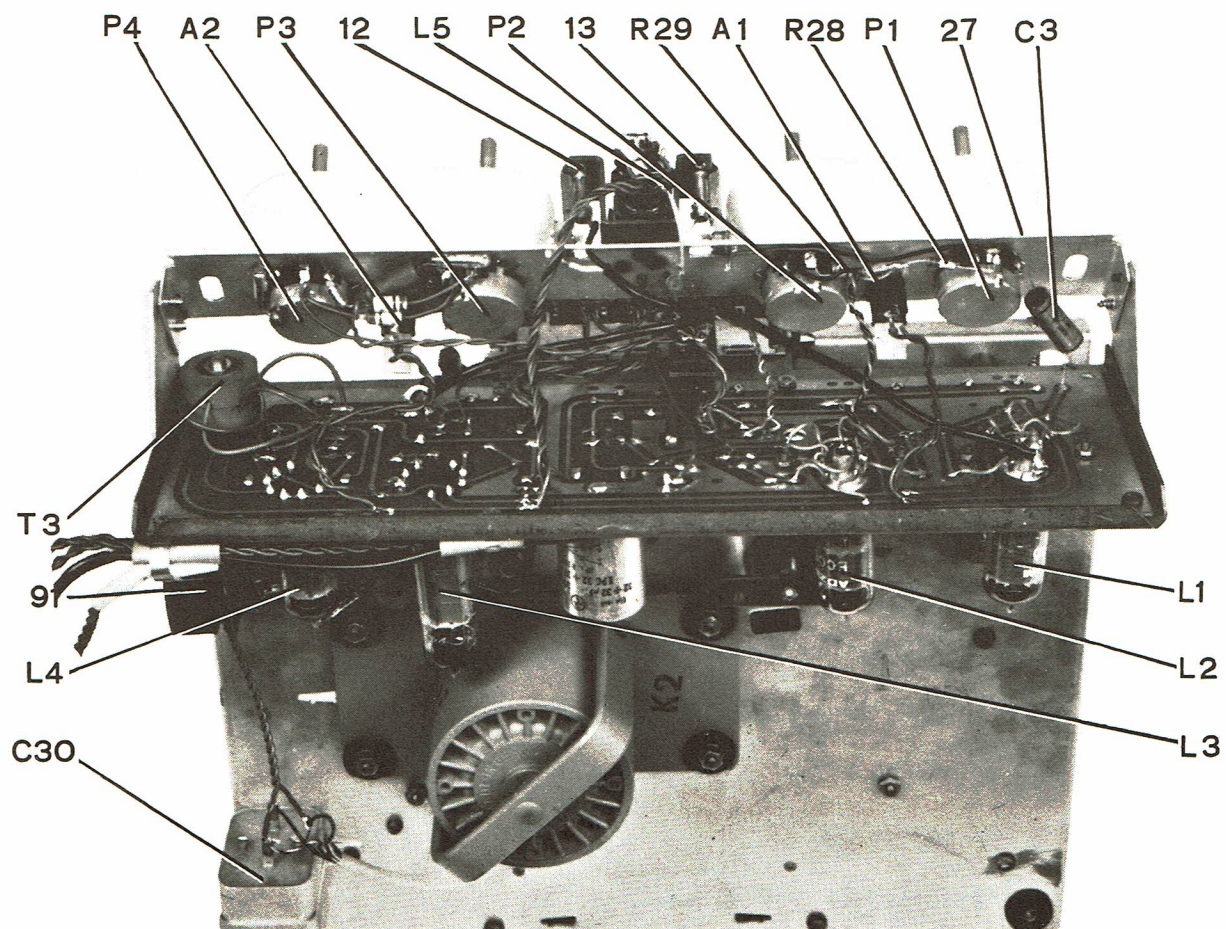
Châssis principal et plaque des circuits imprimés.
